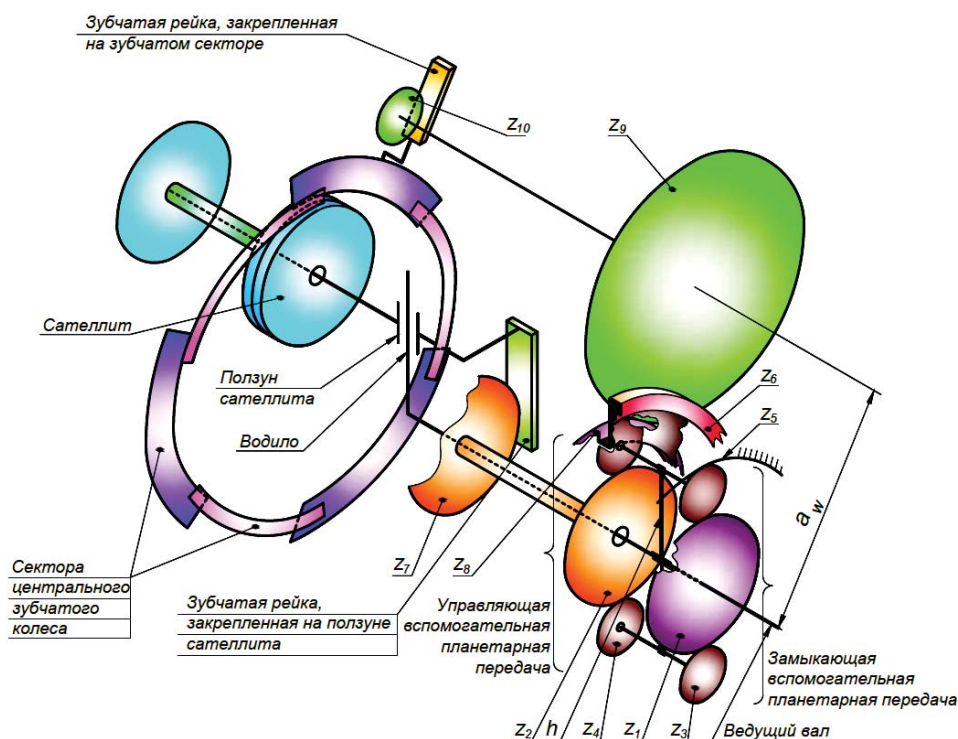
Схема механической передачи механизма регулирования передаточного отношения
